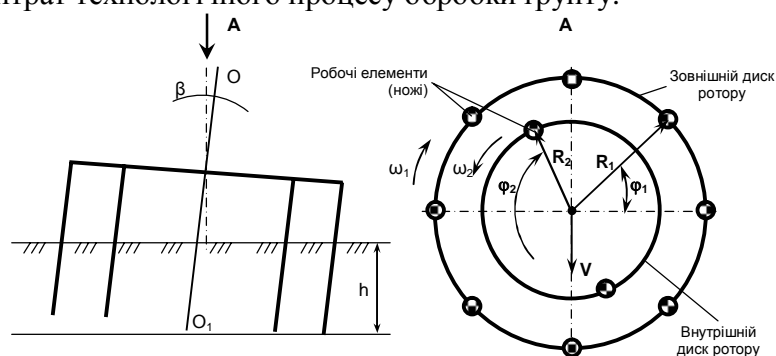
Конструктивно-технологічна схема вертикально-фрезерного адаптера
